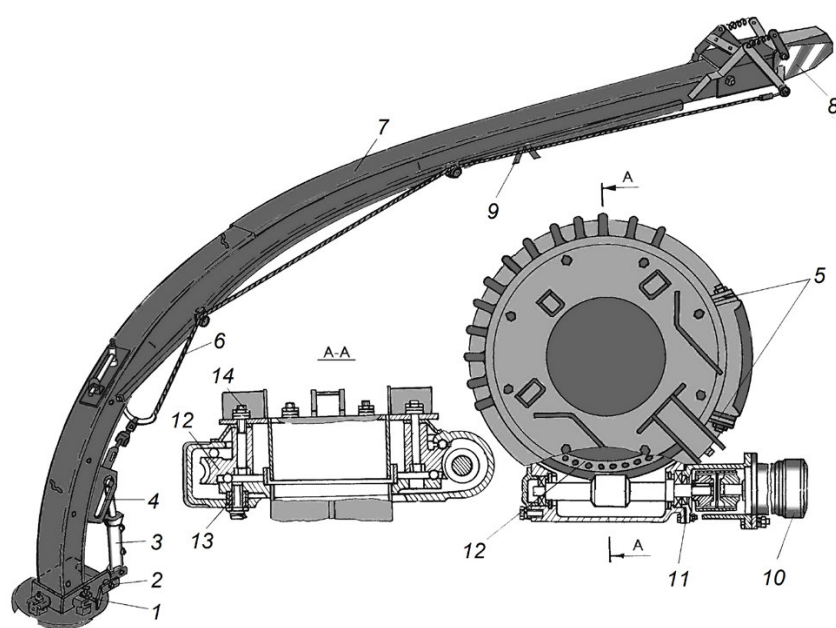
Силосопровод: 1 – болт; 2 – ось; 3 – гидроцилиндр; 4 – кронштейны; 5 – болты крепления; 6 – трос; 7 – желоб; 8 – козырек; 9 – ловители; 10 – гидромотор; 11 – крепление гидромотора; 12 – червячный редуктор; 13 – втулки; 14 – спецболты
